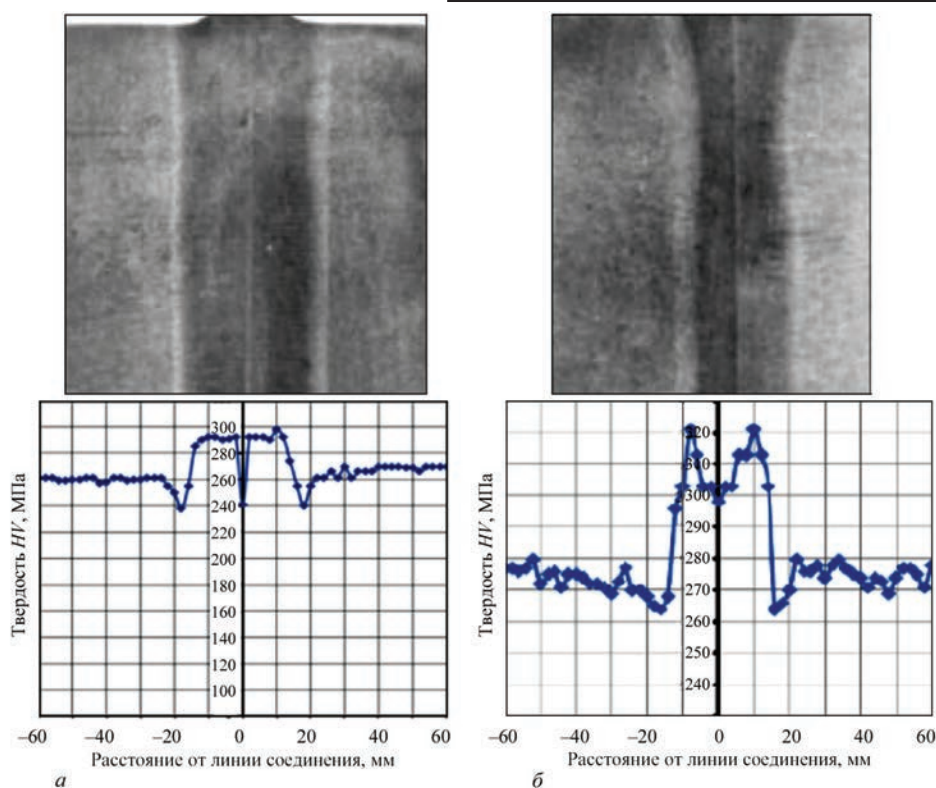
Макрошлифы при оплавлении сварных соединений рельсов М76, сваренных на НО (а) и ПО (б)
